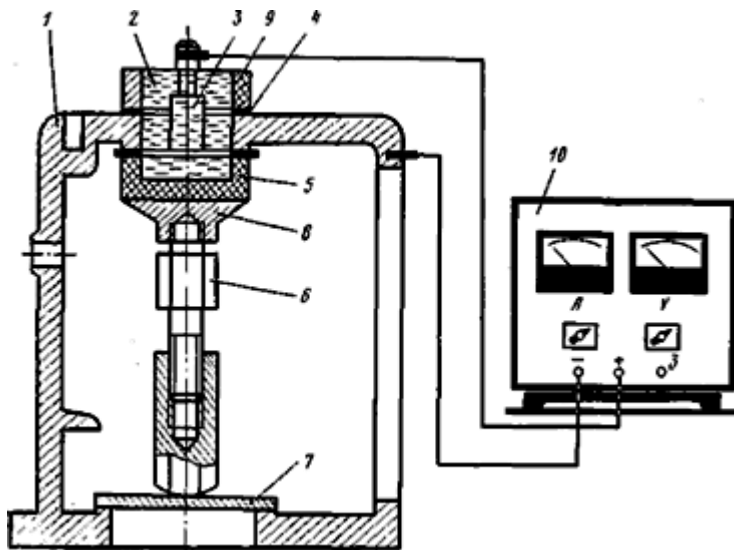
Схема местного осталивания гнезд подшипников картера коробки передач [1]:
